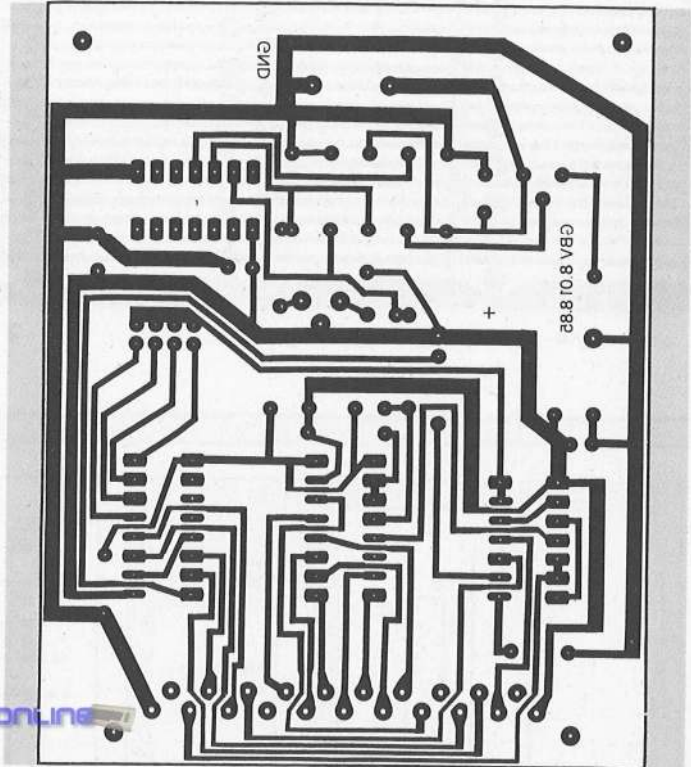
Das Platinenlayout des D-A-Wandlers im Maßstab 1:1 (Lötseite, spiegelverkehrt)
